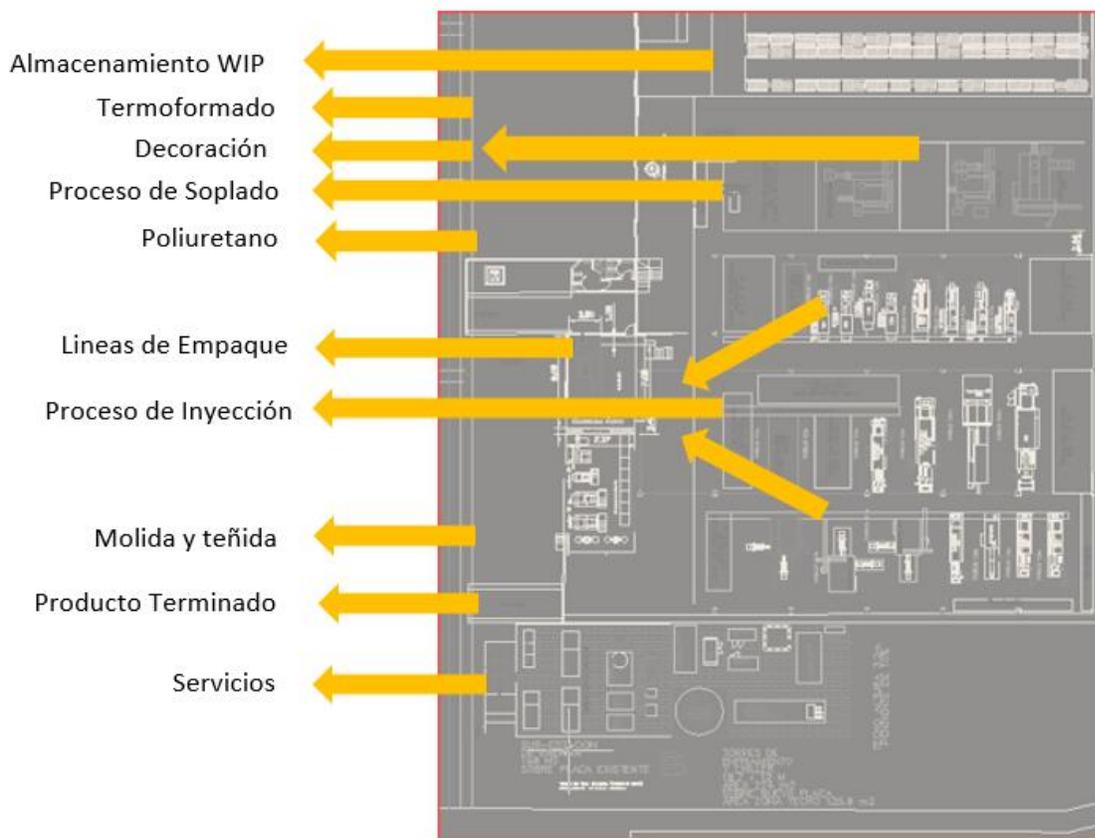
Distribución de Planta Plástico. Fuente: Elaboración propia
